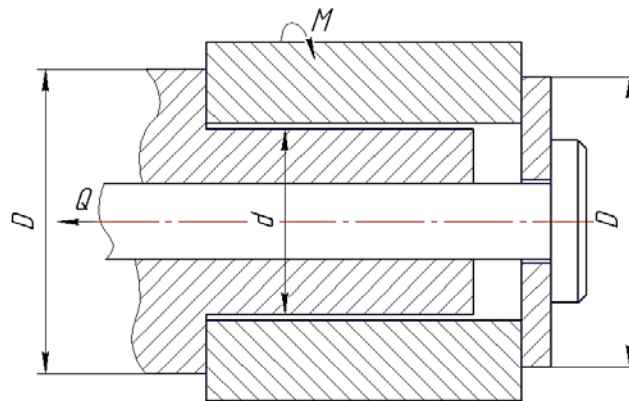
Схема установки заготовки на оправке с зазором и упором в торец
